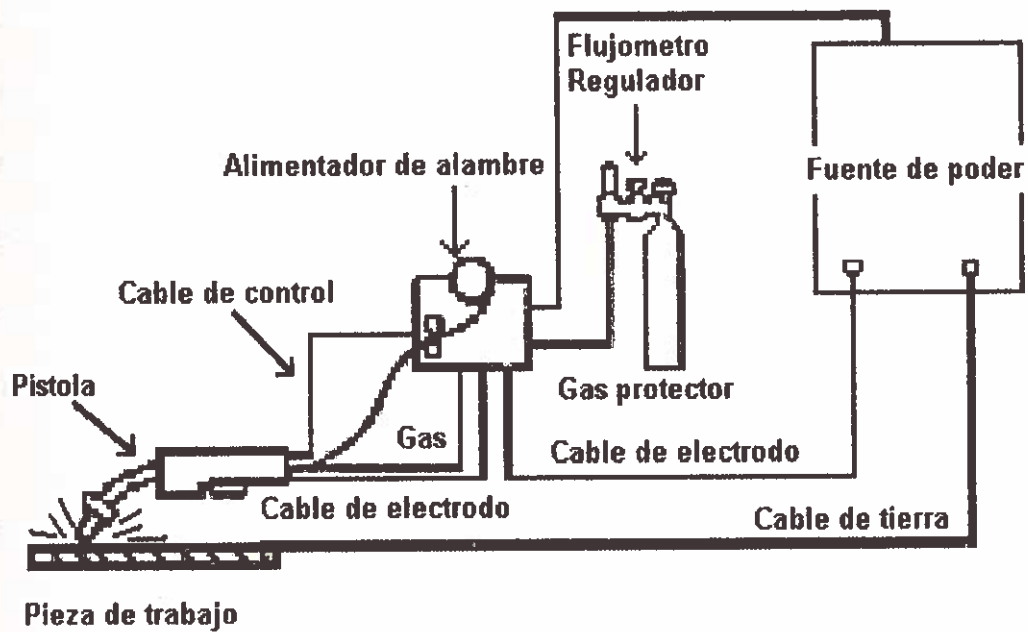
Circuito de soldadura para el proceso GMAW. (Ref. 5).
